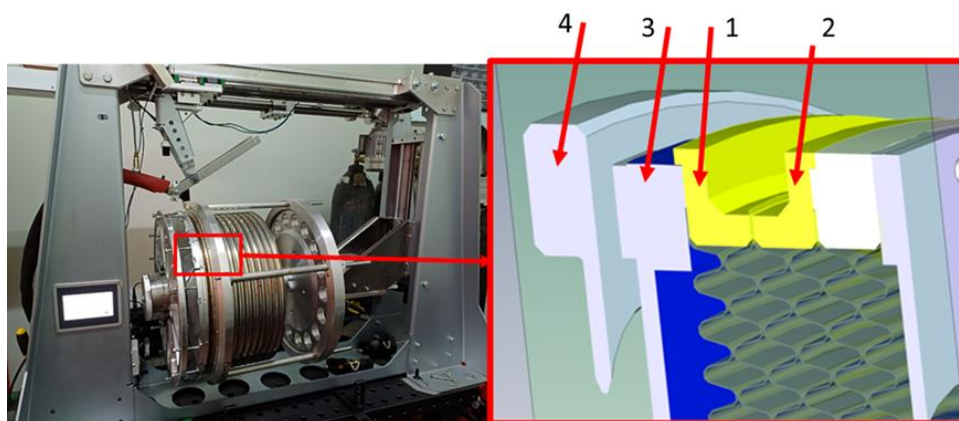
Установка для складання та зварювання зовнішніх кільцевих швів, схематичне розташування зварних секцій (6 шт) у пристрої.
